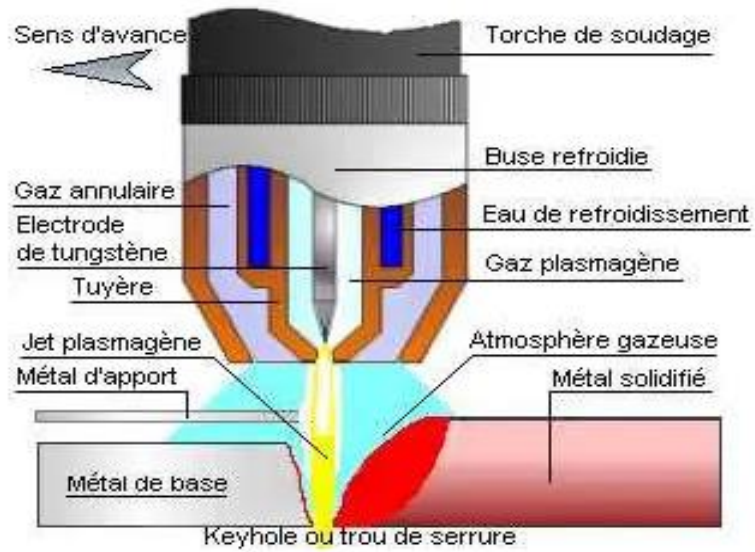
Soudage à l'arc d'aluminium [16]
